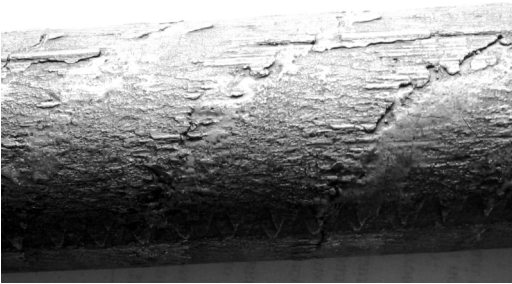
Заготовка со следами спаев фронтов, имеющих наклон к оси заготовки
